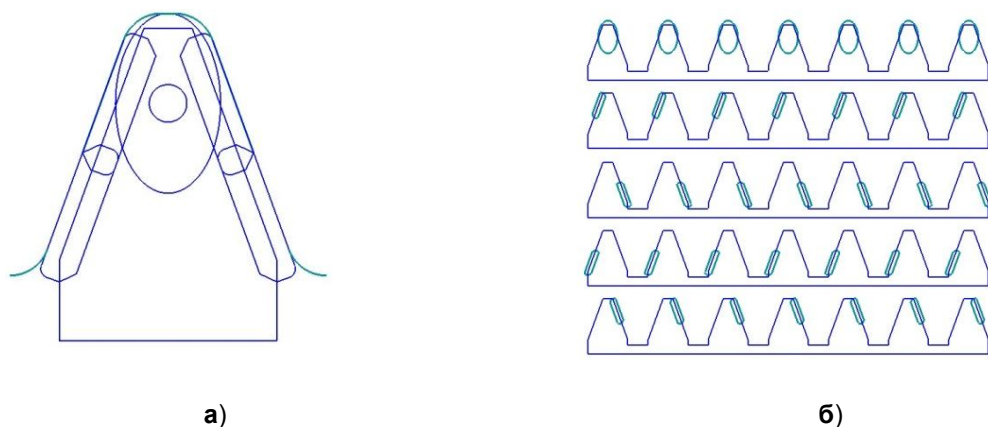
Расположение режущих пластин в корпусе сборной червячной фрезы с применением эллипсной пластины
